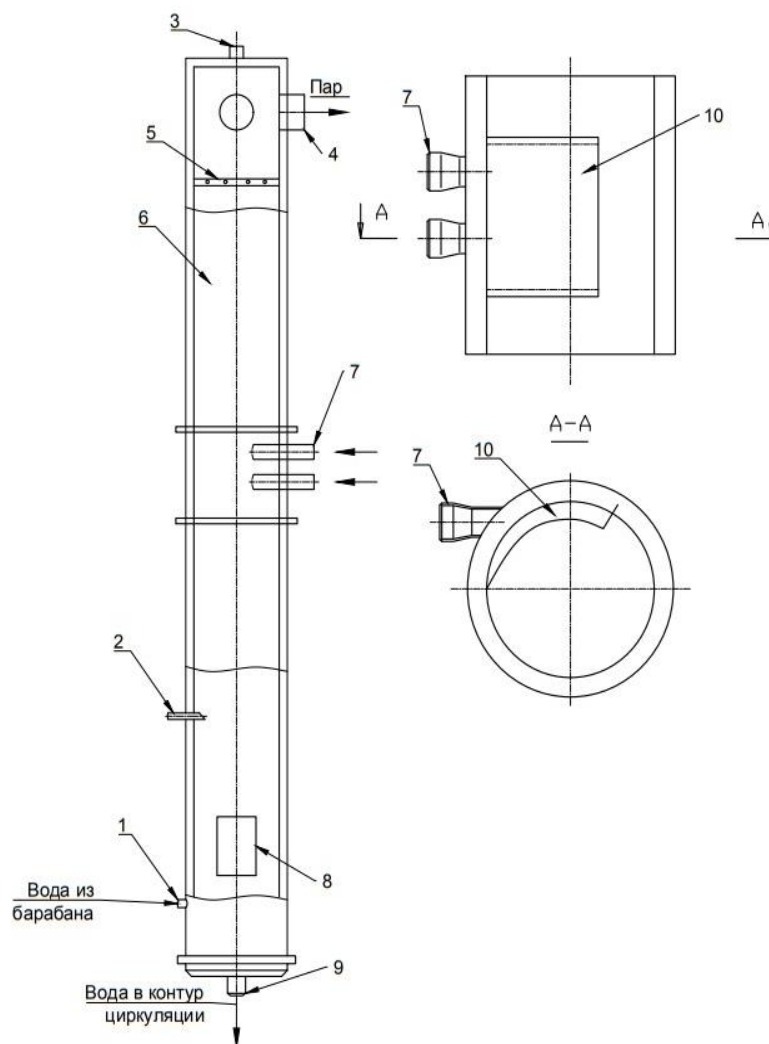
Эскиз принципиального выносного циклона (1 – штуцер для трубопровода, подводящего котловую воду, 2 – штуцер для трубопровода непрерывной продувки, 3 – штуцер для воздушника, 4 – штуцер для пароотводящего трубопровода, 5 – пароприемный дырчатый щит, 6 – корпус, 7 – штуцера для трубопровода пароводяной смеси, 8 – крестовина, 9 – штуцер для водоотпускной трубы, 10 – вставка для образования улитки)
